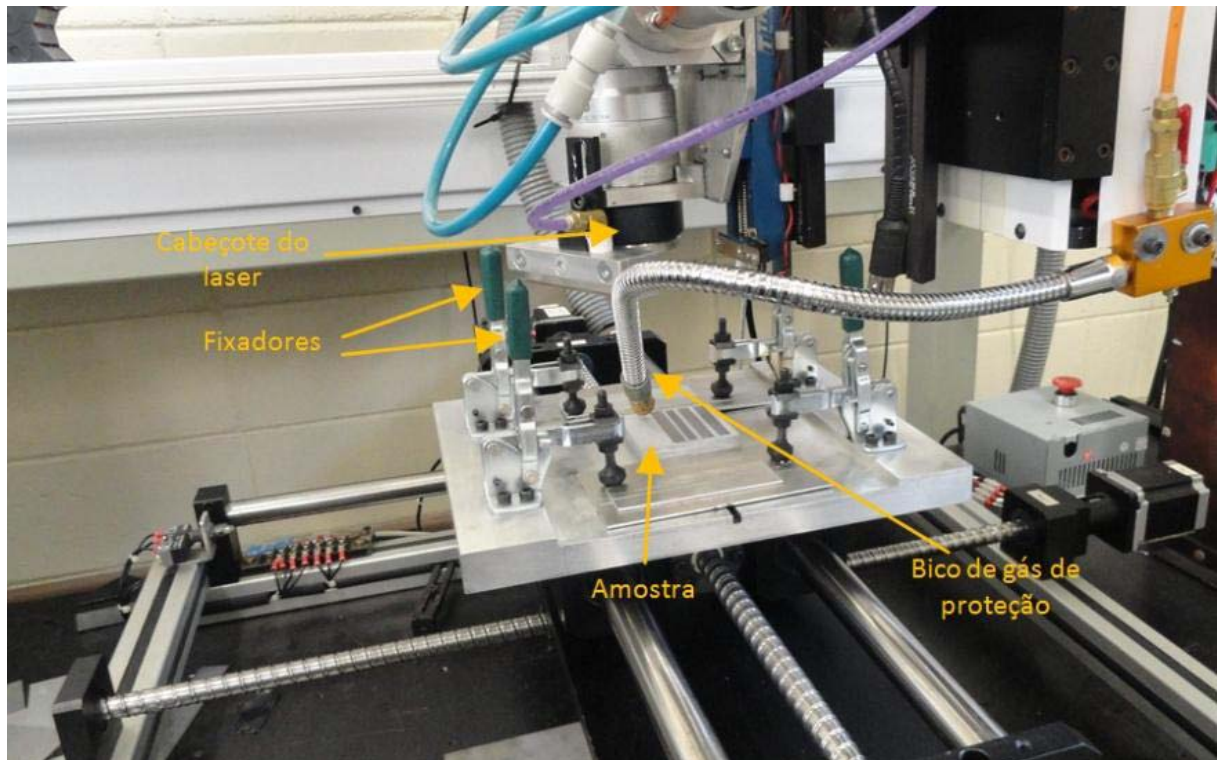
Equipamento a laser utilizado e os seus principais componentes em destaques (5)
